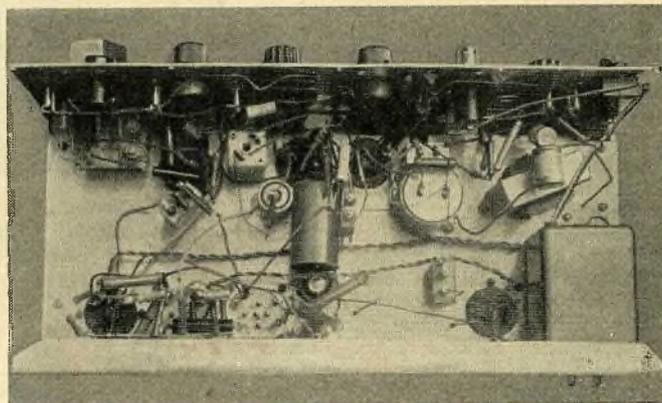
Ein Blick unter das Chassis des Universal-Prüfgerätes zeigt die Verdrahtung.
